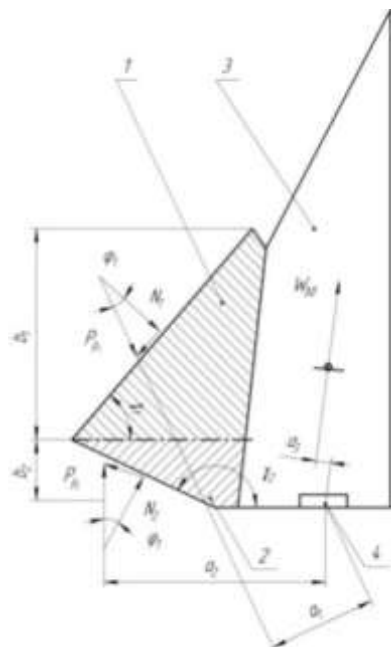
Розрахункова схема лемеша пуга-букера розробки ДДАЕУ:
